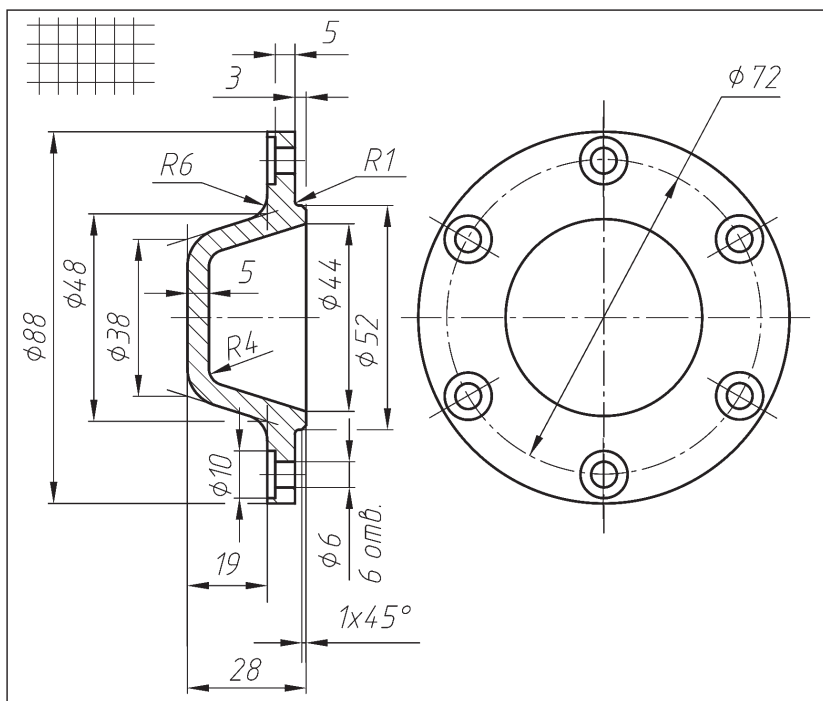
Эскиз детали «Крышка» с натурального образца
